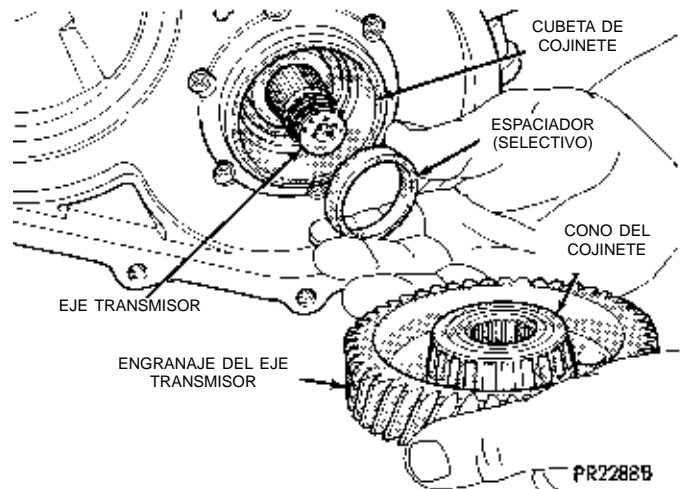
Engranaje de eje transmisor y espaciador (selectivo)
